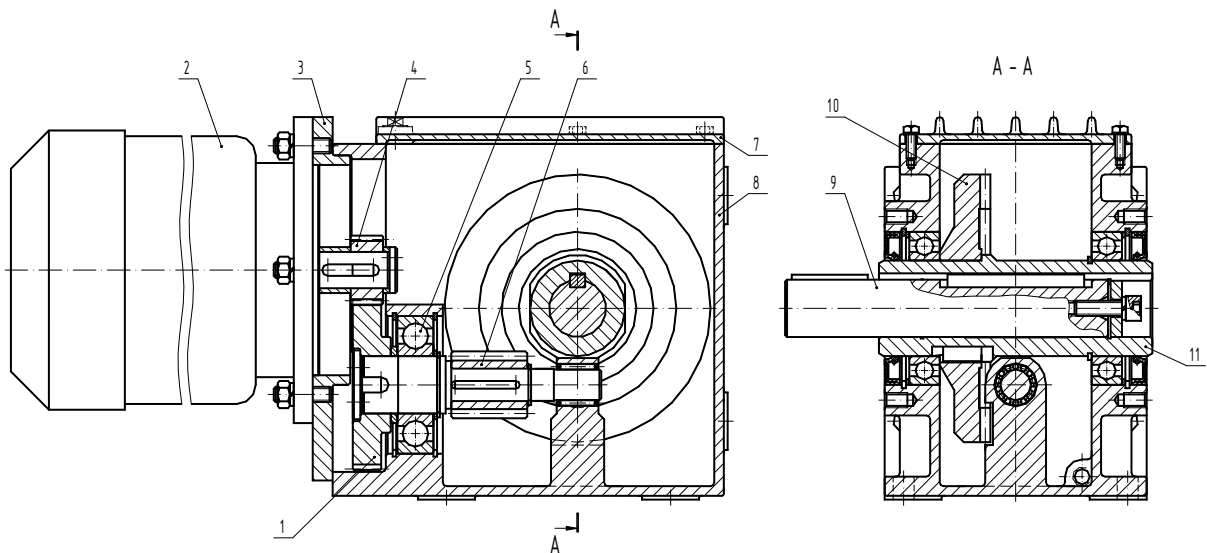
Особенности конструкции универсального цилиндро-спироидного мотор-редуктора МРЦ.СП 60.40
